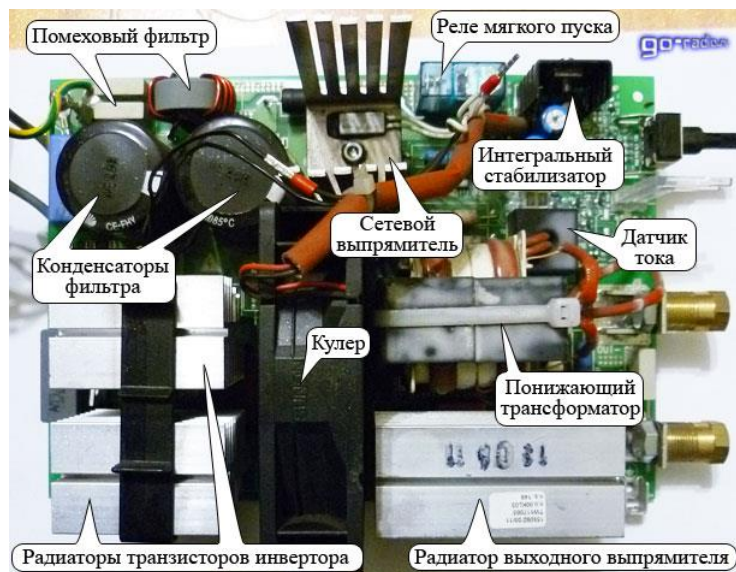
Внутреннее устройство сварочного инвертора
